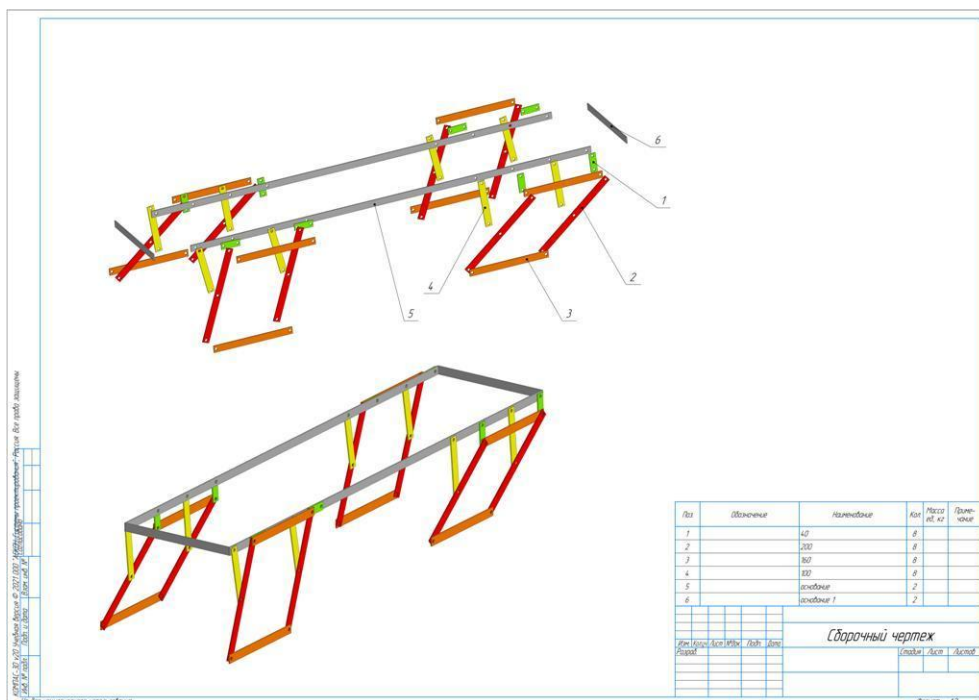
Сборочный чертёж шагающей машины (перевернуто).
